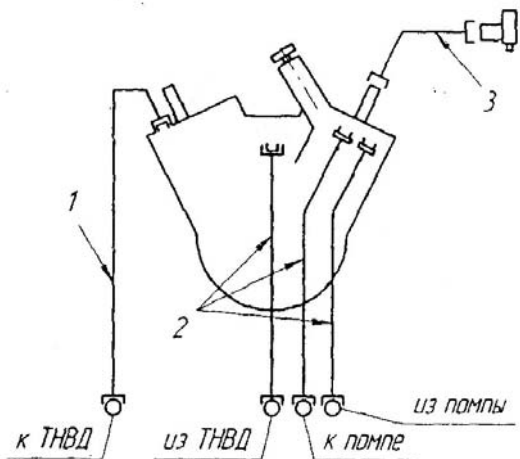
Схема соединения топливопроводов при испытании ТНВД двигателя ЯМЗ-740 со штатным топливоподкачивающим насосом:
